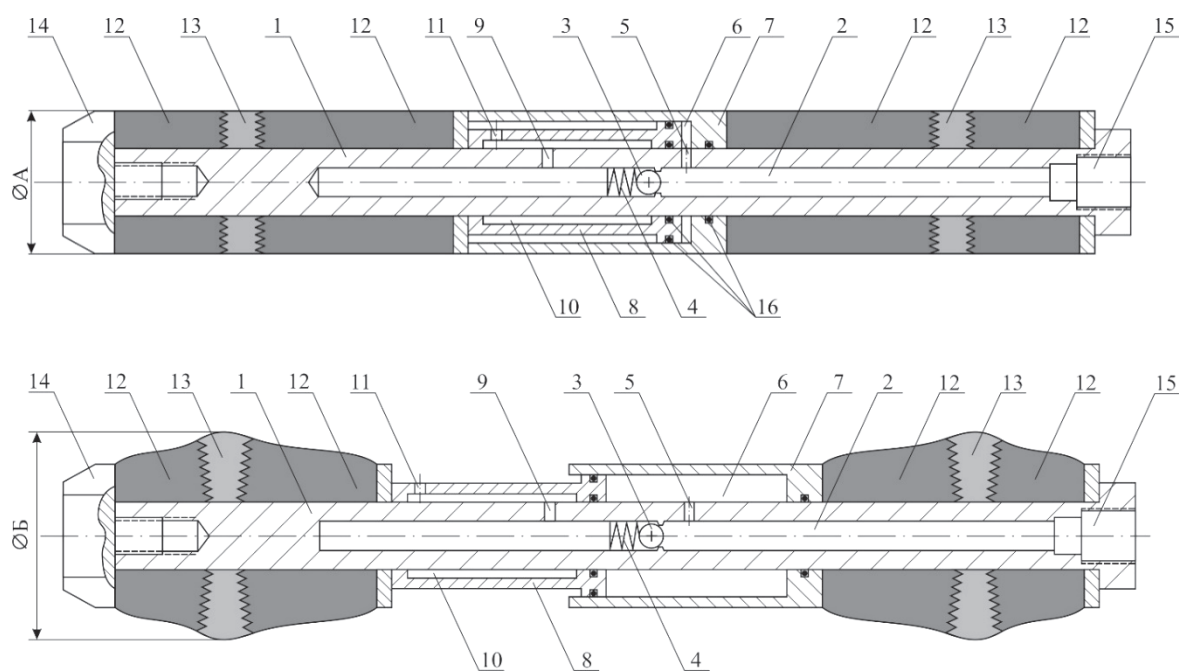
Схема перспективного полиуретанового уравновешенного герметизирующего устройства. 1 — корпус; 2 — канал; 3 — шарик; 4 — пружина; 5 — радиальное отверстие; 6 — рабочая камера; 7 — цилиндр; 8 — поршень; 9 — радиальное отверстие; 10 — проточка; 11 — радиальное отверстие; 12 — уплотнительный элемент; 13 — вставка; 14 — стопорящая гайка; 15 — гнездо; 16 — кольцевое уплотнение.
